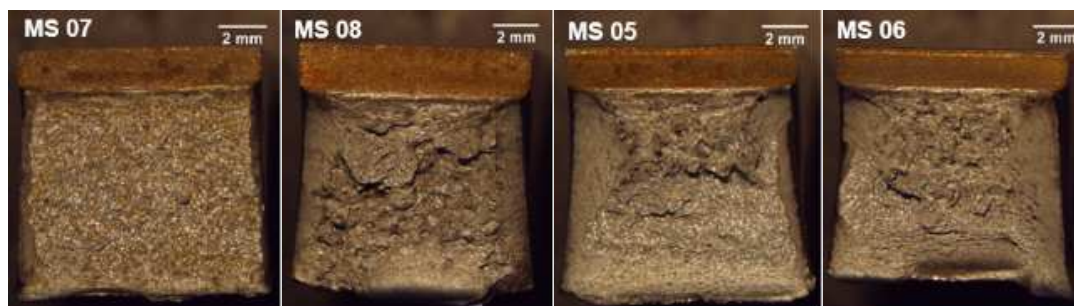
Amostra da superfície de fratura das amostras com o entalhe sobre a zona de solda
